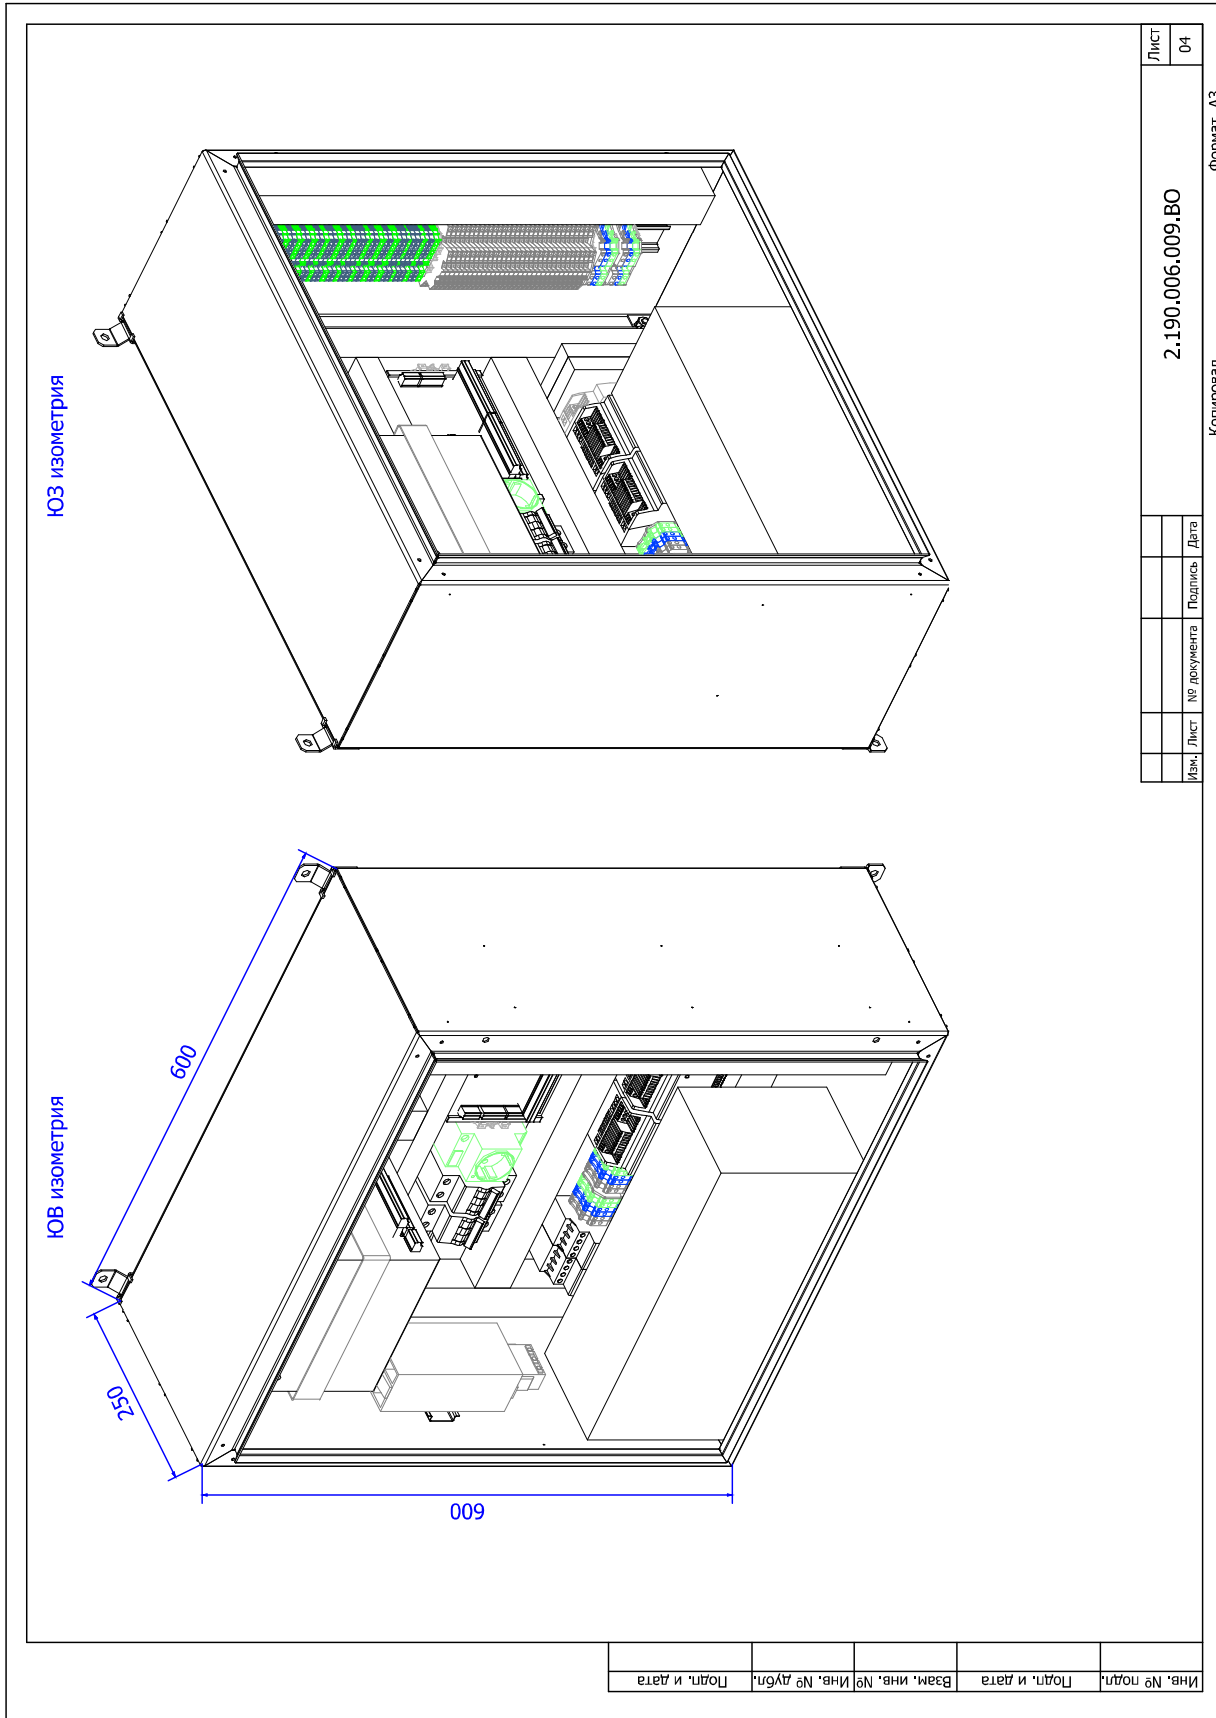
Шкаф ARIS. Внешний вид в изометрии и габаритные размеры
